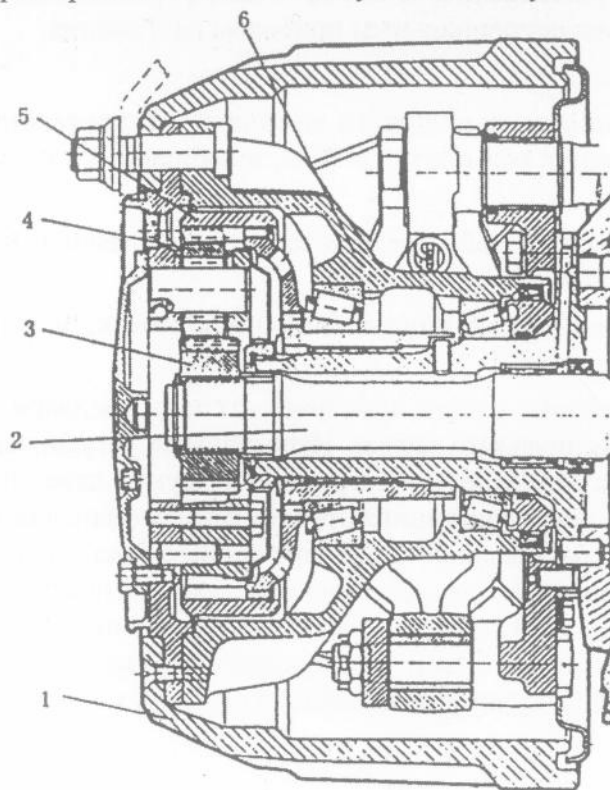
Конструкция ободочного редуктора приводной оси
